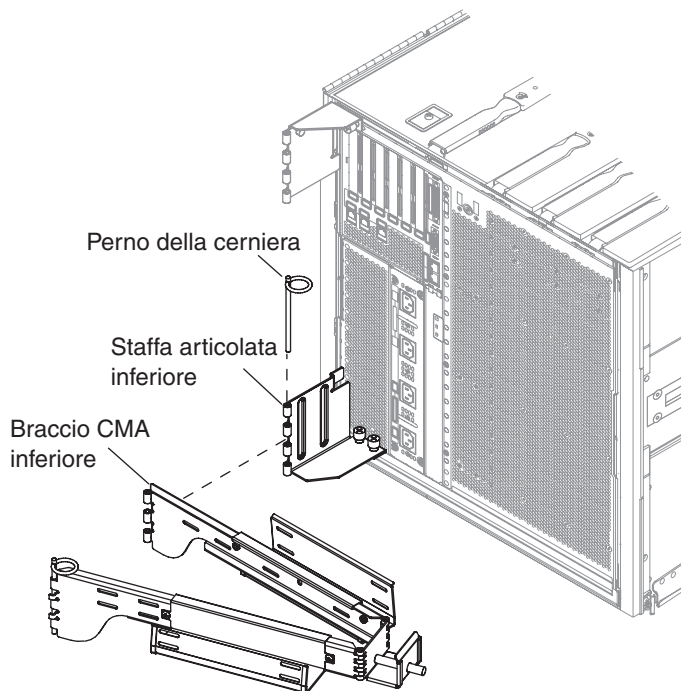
Collegamento del braccio CMA inferiore e della staffa articolata
